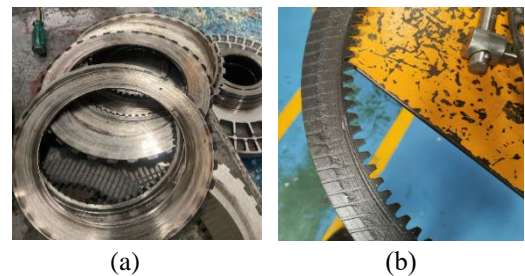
(a) Patahan spring dumper holder plate membentuk brittle fracture (b) Kerusakan pada spring dumper
